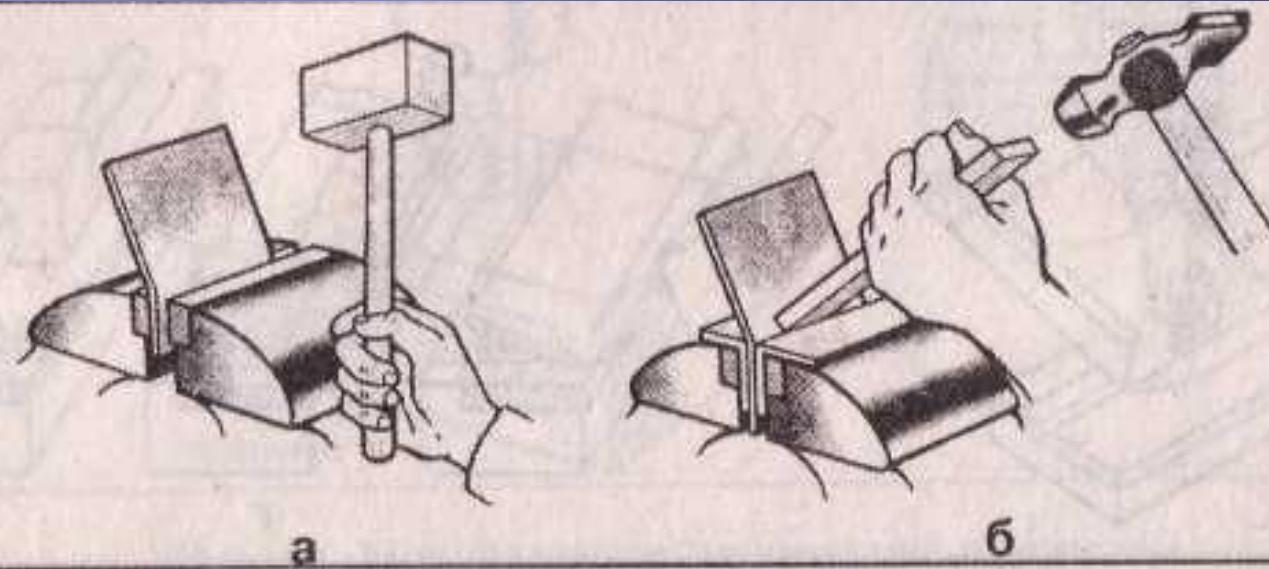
Сгибание заготовок из тонколистового металла в тисках:
